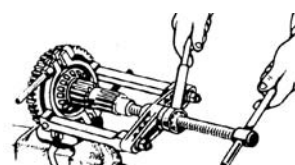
Спресовка внутренней обоймы подшипника № 67512K1 с вторичного вала.
